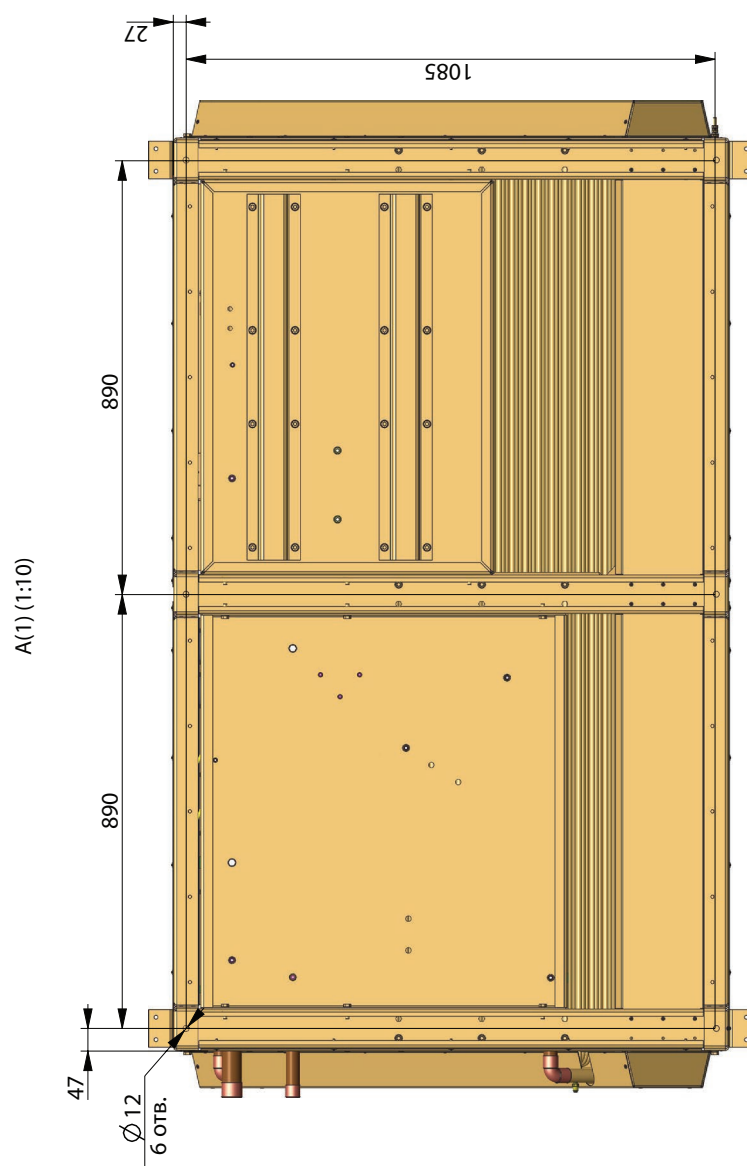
Агрегат компрессорный МАКК 120-621, -781
